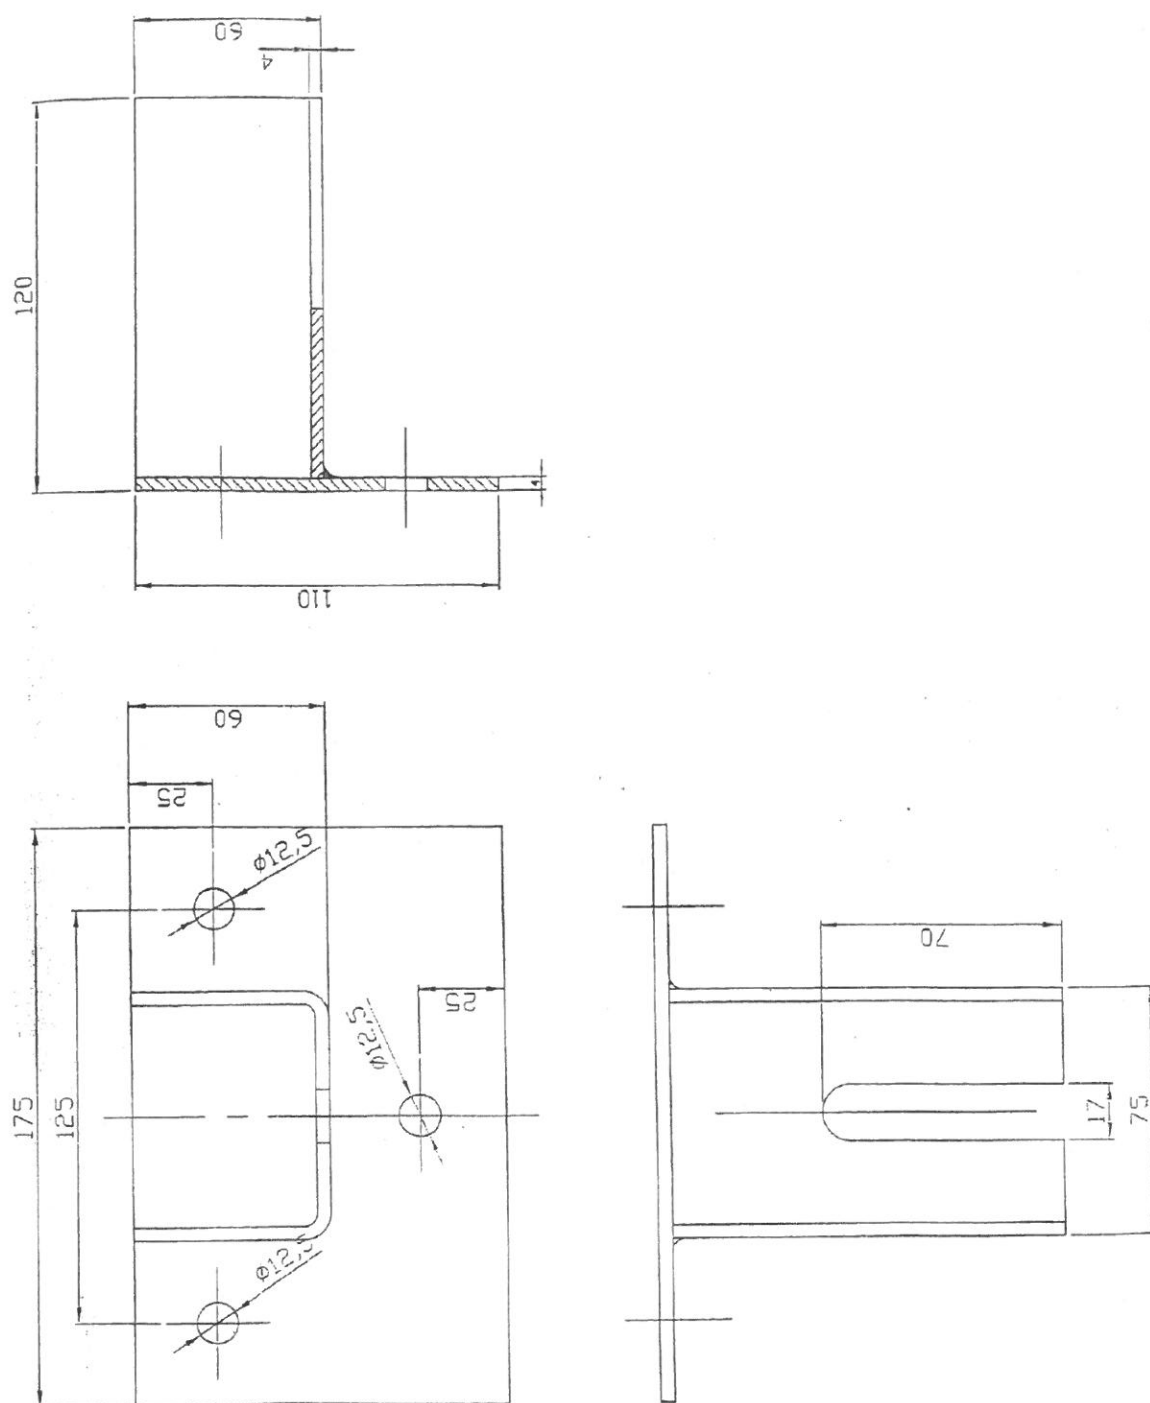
Brama przesuwna N80 – szczegóły konstrukcyjne krawędzi poziomych skrzydeł
